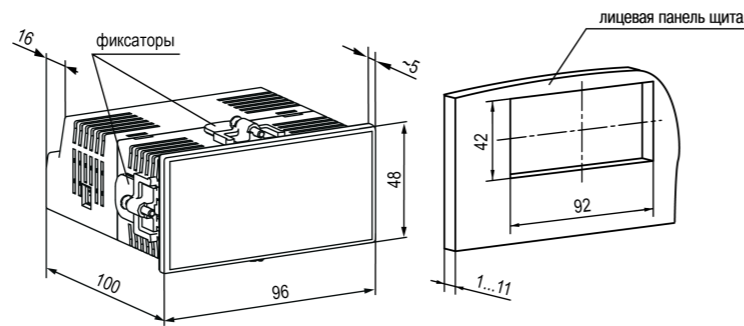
Габаритные размеры корпуса Щ2 и монтажного отверстия в щите
